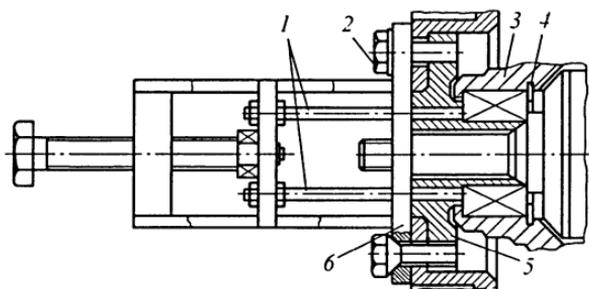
Приспособление для снятия ступиц передних и задних колес автомобилей: 1 — штифты, упирающиеся во внутреннее кольцо подшипника; 2 — болты крепления фланца к ступице; 3 — поворотный кулак; 4 — стопорное кольцо; 5 — ступица; 6 — фланец; 7 — винт, упирающийся при выпрессовке ступицы в торец хвостовика наружного шарнира привода переднего колеса либо в торец цапфы балки (при выпрессовке ступицы заднего колеса)
